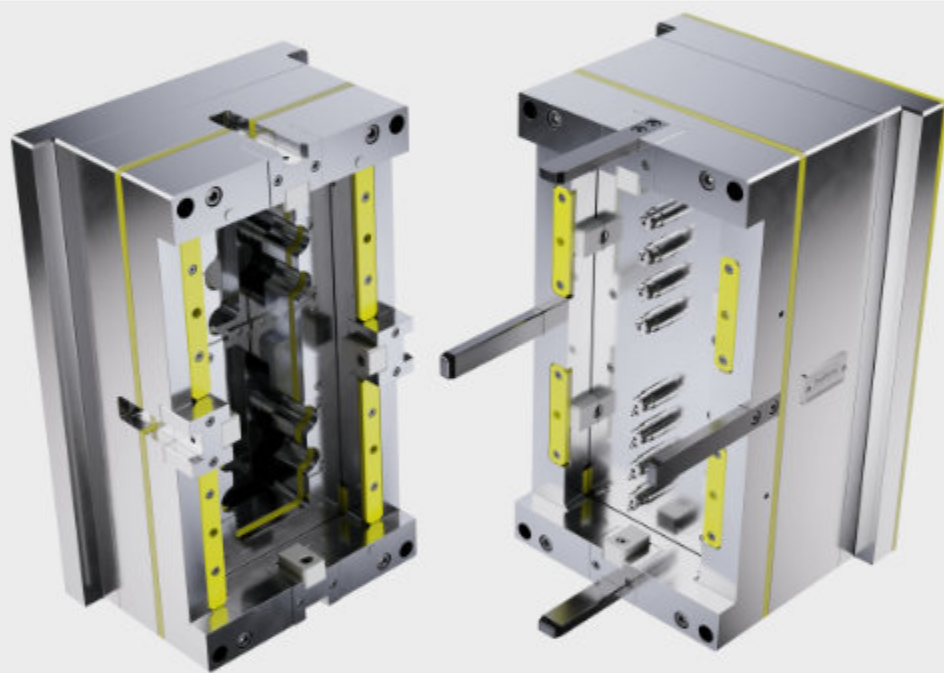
IsoForm®-Werkzeug ohne Kontur
